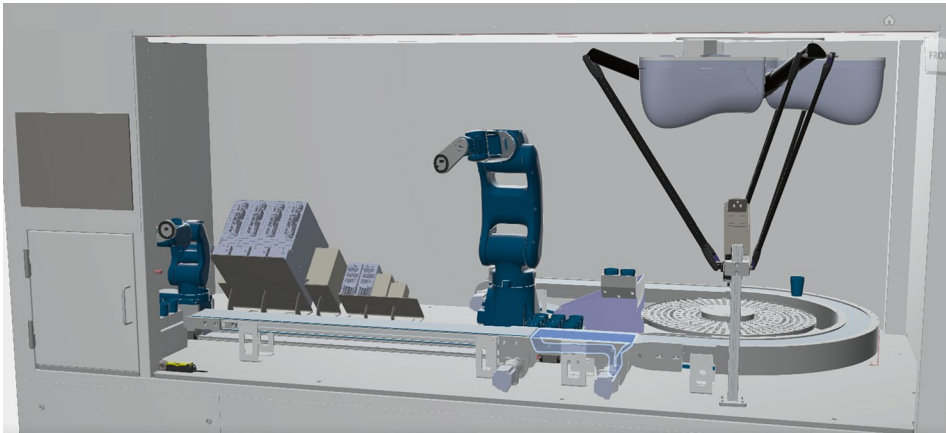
CAD-Zeichnung Rotary Table Dispenser System
